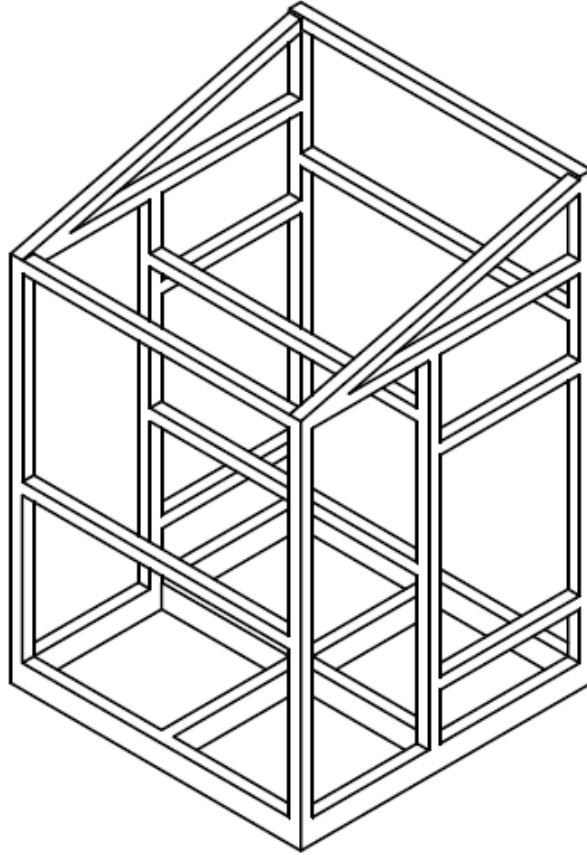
Estructura metálica soldada con perfil 40x40x2 mm.
